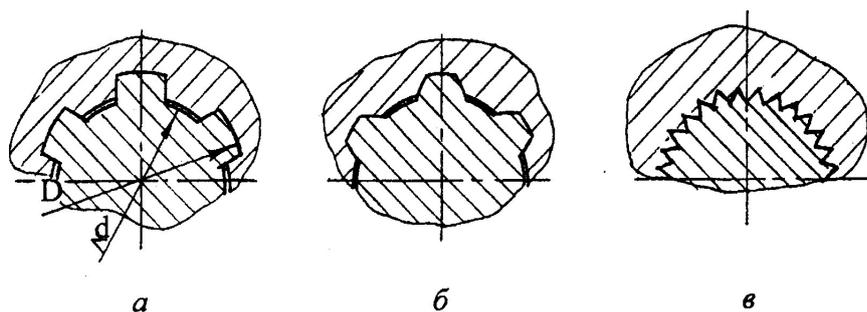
Разновидности шлицевых соединений по форме профиля зуба
